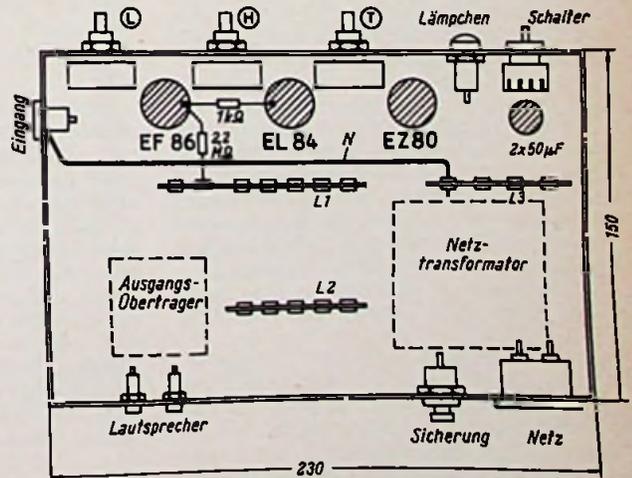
Chassis-Ansicht von unten. Die Chassis-Tiefe beträgt 60 mm
